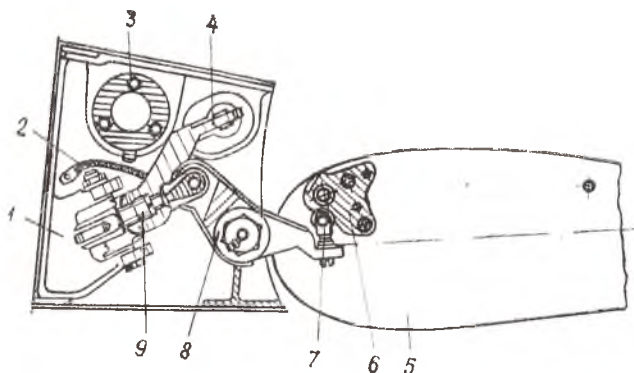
Дифференциальный механизм в системе управления элерон-интерцепторами: 1—кронштейн; 2—перемычка металлизации; 3—направляющая тяги элеронов; 4—качалка; 5—элерон; 6—упор; 7—вилчатый болт с роликом; 8—качалка; 9—тяга-тандер
